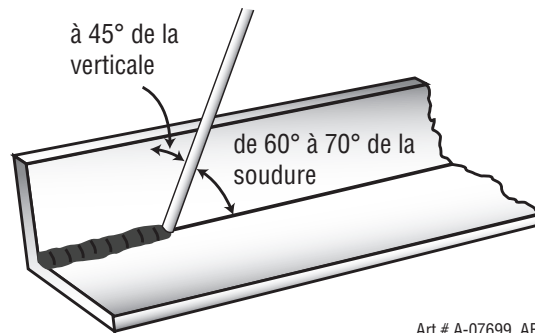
Position de l'électrode pour une soudure d'angle HV
